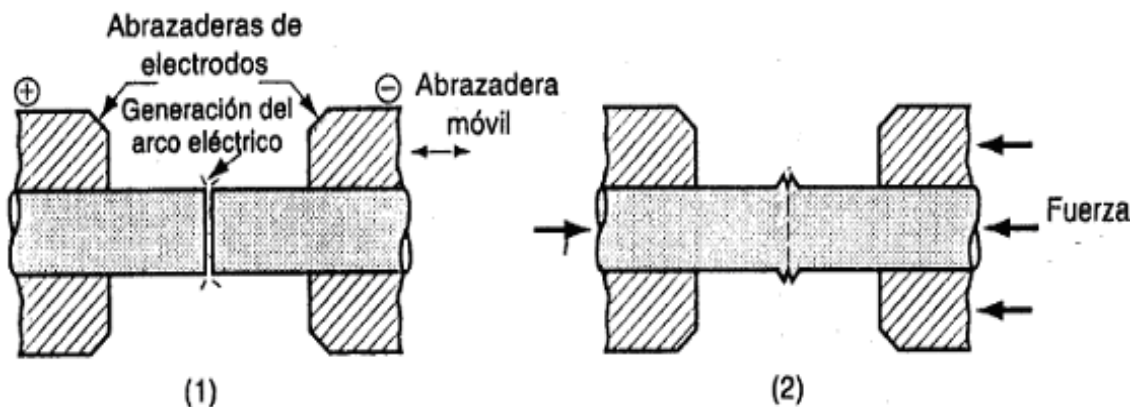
Soldadura por resistencia de chispa
